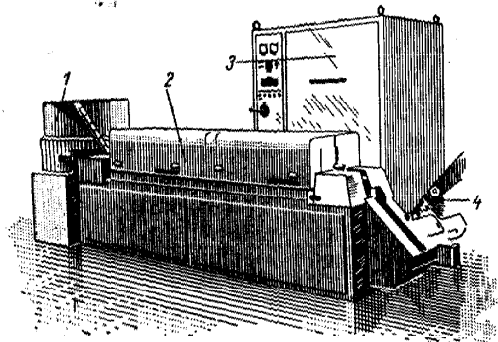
Общий вид нагревателя фирмы «АЕГ» для нагрева заготовок подшипниковых колец:
